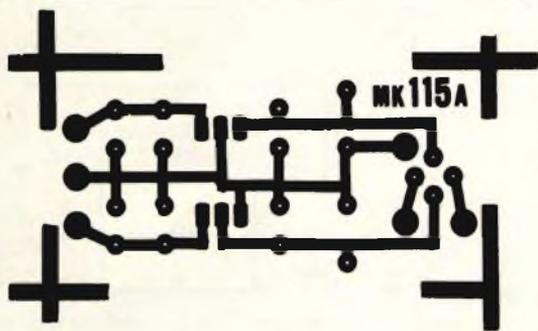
Lato componenti e complessivo montaggio del sistema MK 115.
